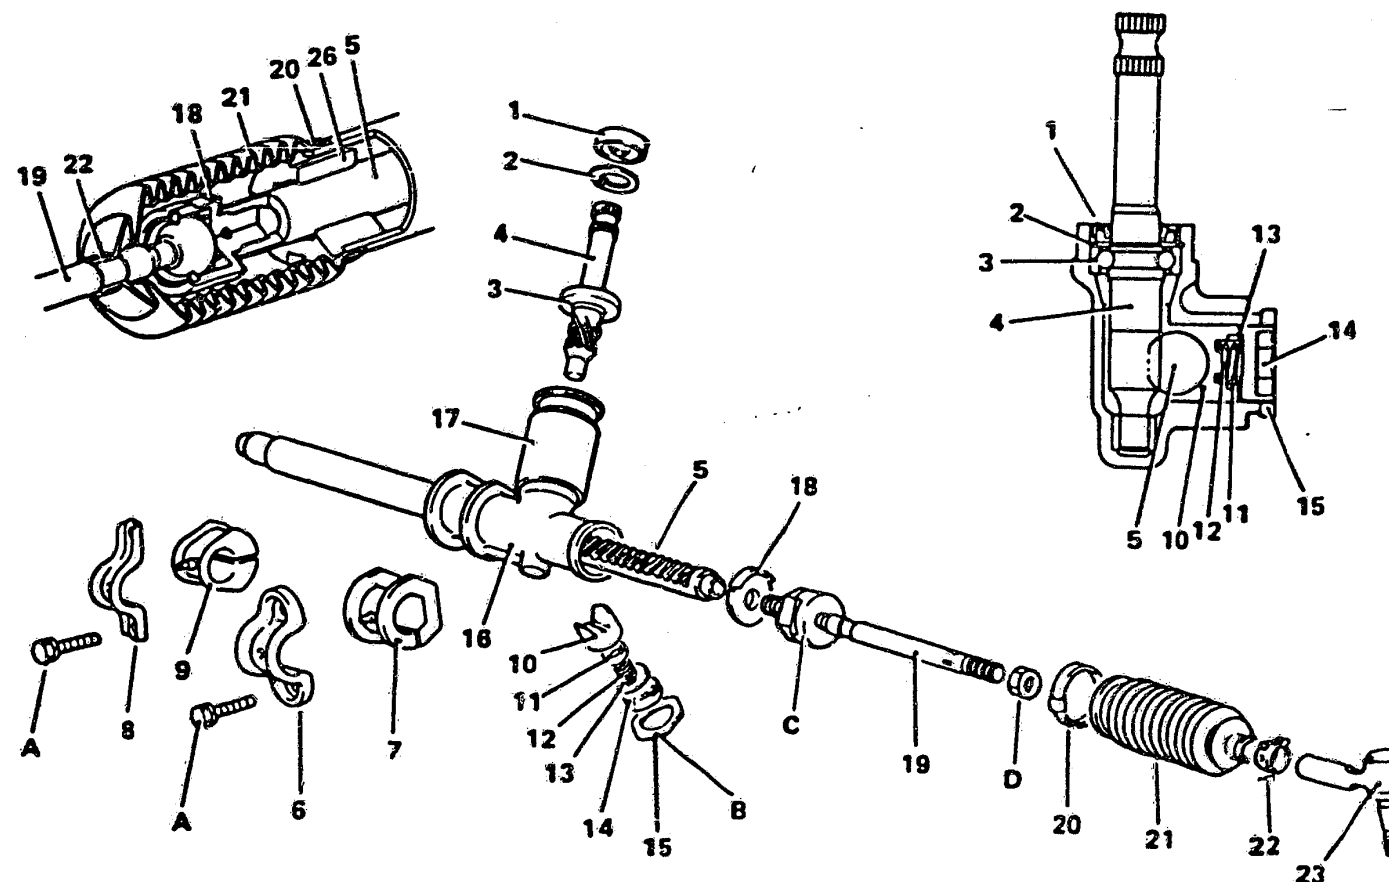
Einzelteile des Zahnstangen-Lenkgetriebes: 1 Wellendichtung – 2 Sprengring – 3 Lager – 4 Ritzel – 5 Zahnstange – 6 Brücke für Lenkgetriebegehäuse – 7 Gummidämpfer – 8 Brücke für Gehäuseende – 9 Gummidämpfer – 10 Stützjoch – 11 Gummischeibe – 12 Jochfeder – 13 Tellerfeder – 14 Jochverschluss – 15 Sicherungsmutter – 16 Lenkgetriebegehäuse – 17 Gelenkabdeckung – 18 Sicherungsblech – 19 Spurstange – 20 Band – 21 Faltenbalg – 22 Schelle – 23 Spurstangenende – 26 Zahnstangenbuchse.
